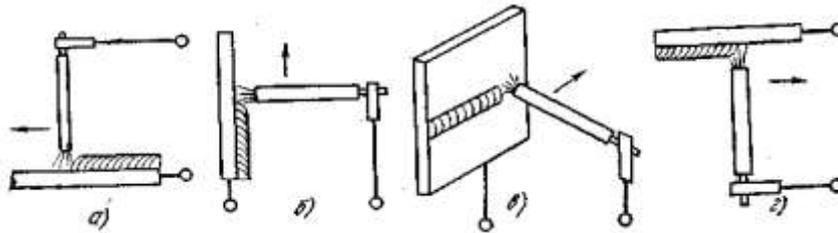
Возможные пространственные положения при ручной сварке.
